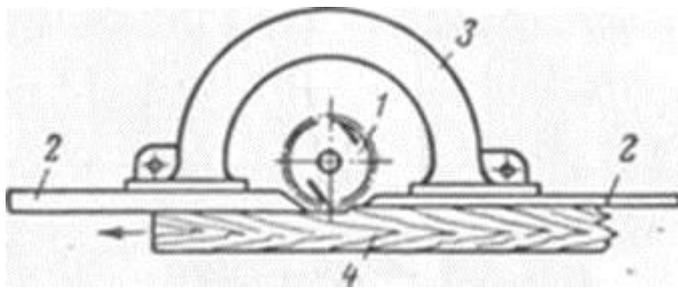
Направляющая линейка фрезерного станка: 1 — ножевой вал, 2 — линейка, 3 — скоба, 4 — обрабатываемая деталь
